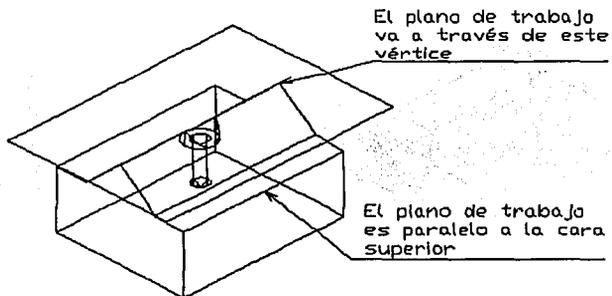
Plano de trabajo restringido a un eje y paralelo a un plano (On Vertex & Planar Parallel).
